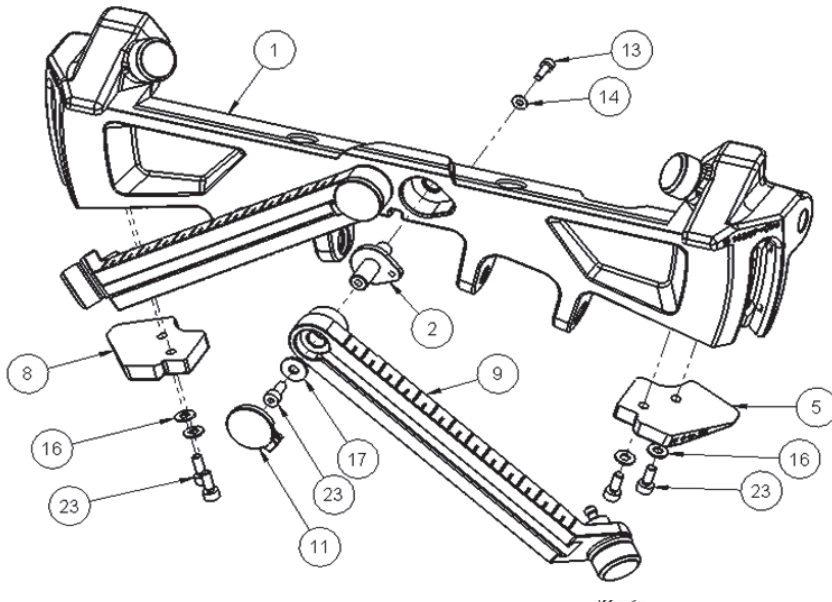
Vista explodida do conjunto frontal – parte 1
